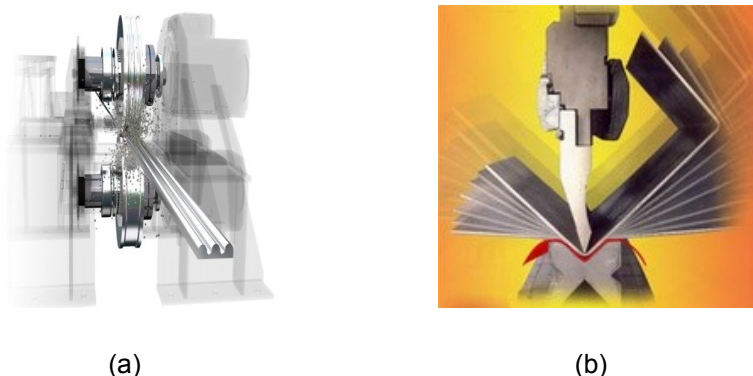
Processos de enformagem a frio: (a) laminagem a frio; (b) quinagem.
